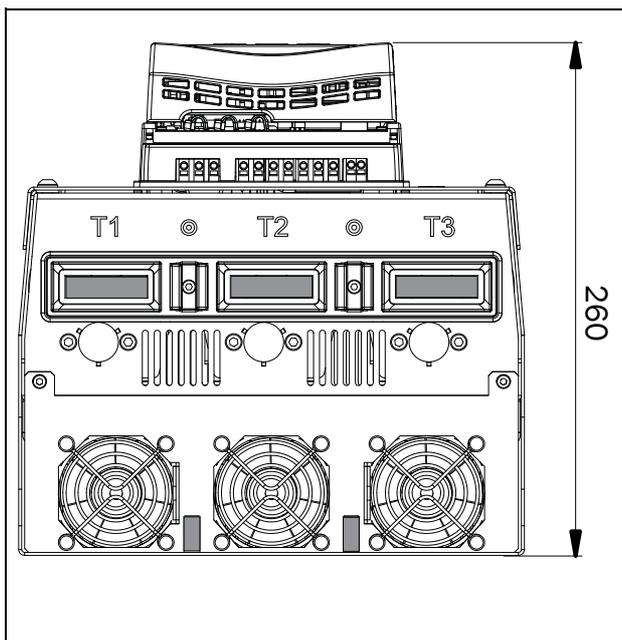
Габаритные размеры Emotron TSA типоразмера 4, вид снизу.
